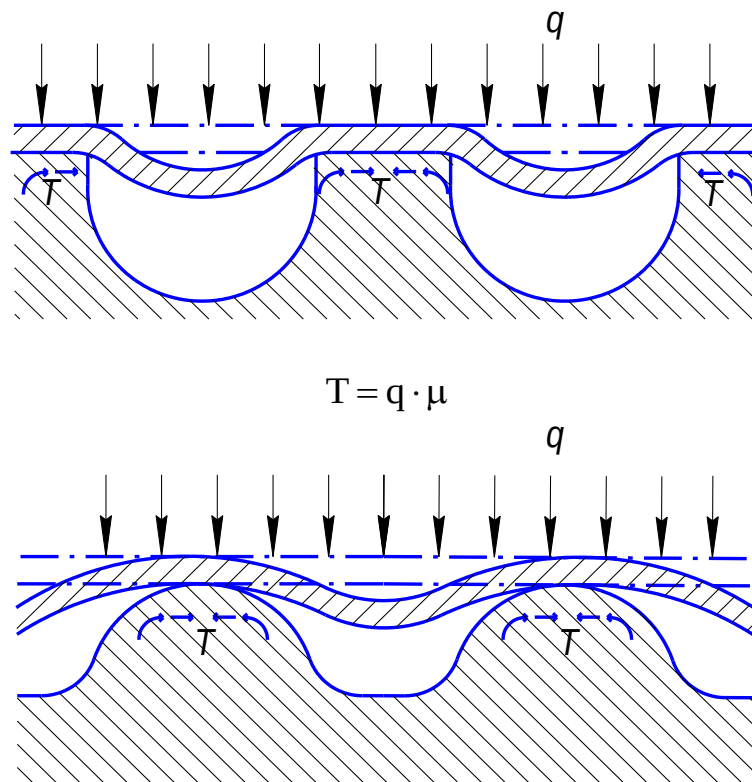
Схеми процесів формозмінювання під час штампування рифту по жорсткій матриці (а) та пуансону (б)
